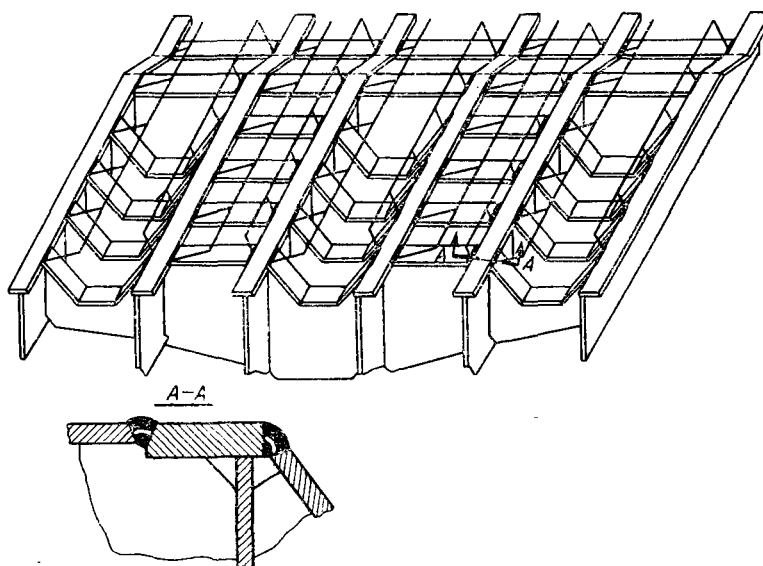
Сварная рама под двигатель внутреннего сгорания
